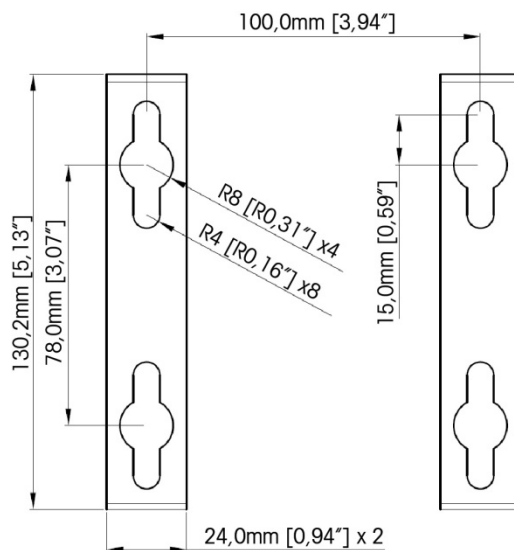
Padrão dos Orifícios de Montagem na Parede com Suporte (VESA 100 x 100mm) (em terminais IND570 fabricados depois de abril de 2016)
